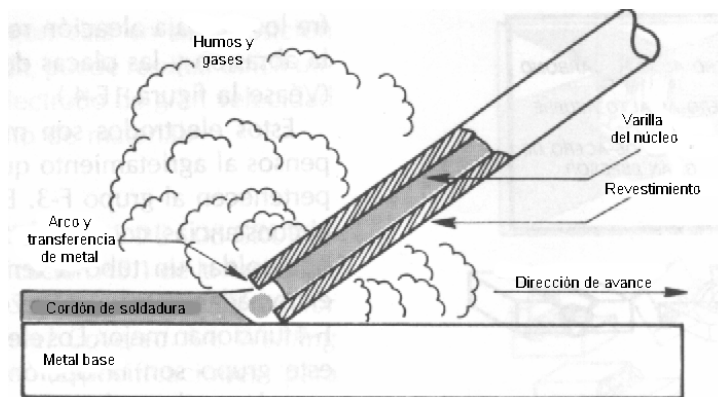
Soldadura por arco de metal protegido
